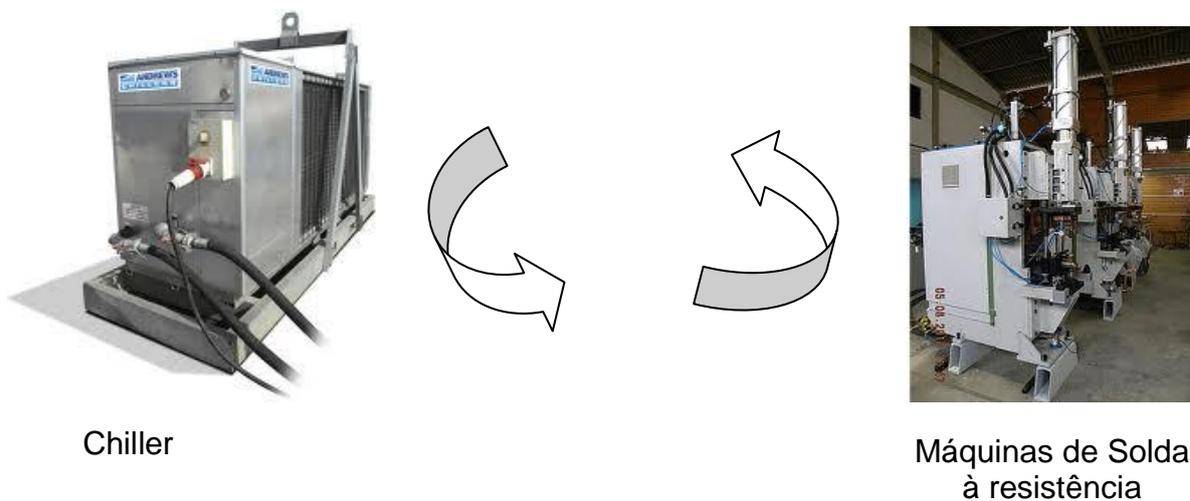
Esquema simbólico da refrigeração das máquinas de Solda.
